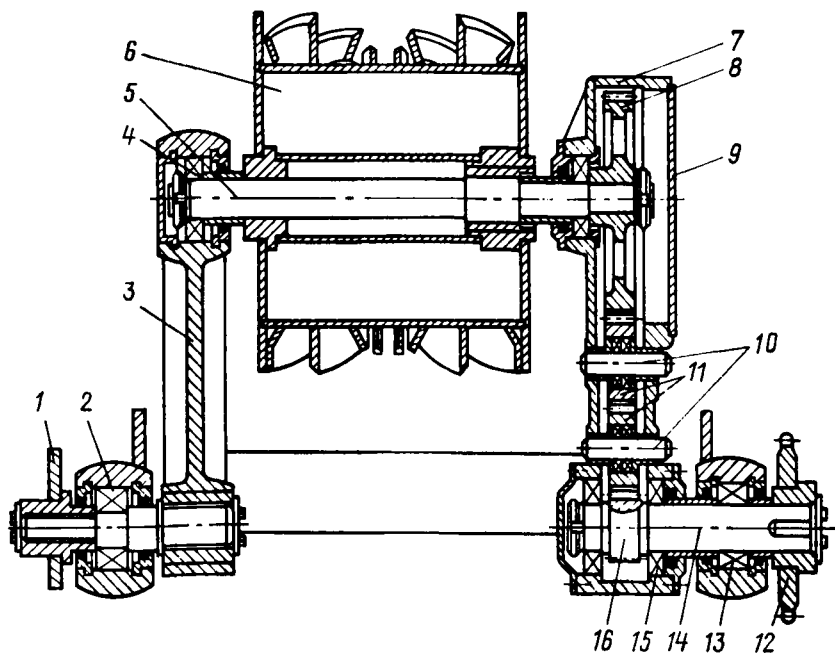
Окорочная головка станка 20К80-1:
